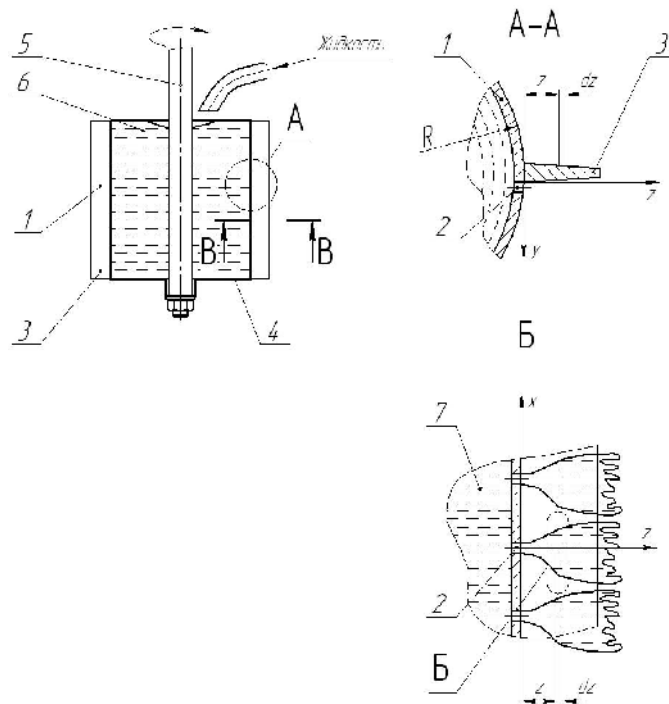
Схема и принцип работы веерного роторно-пленочного устройства
